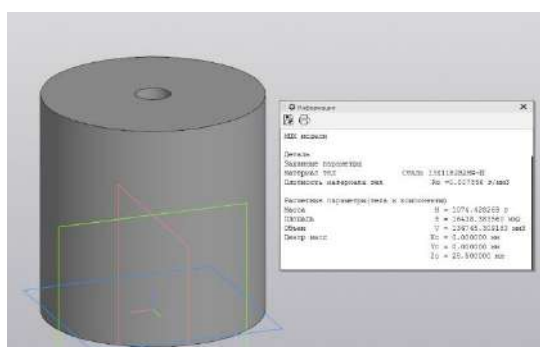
3D модель заготовки отриманої з трубного прокату
